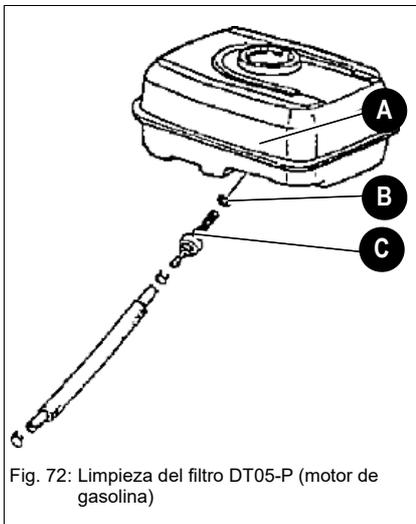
Limpieza del filtro DT05-P (motor de gasolina)
